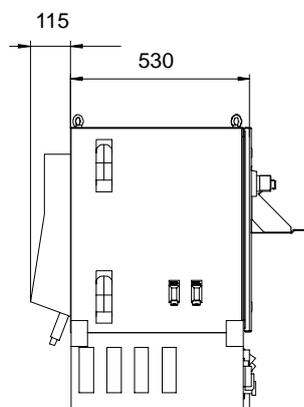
Armoire avec ventilateur à l'arrière, y compris dimensions et connexion des câbles (dimensions en mm)
